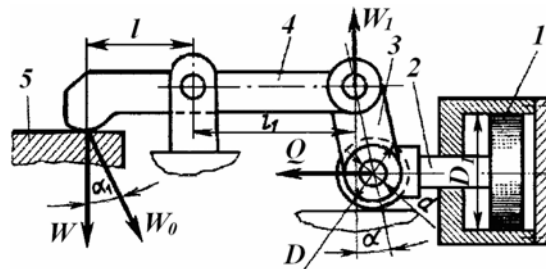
Конструктивная схема рычажного шарнирного усилителя зажимного устройства с пневмоцилиндром
